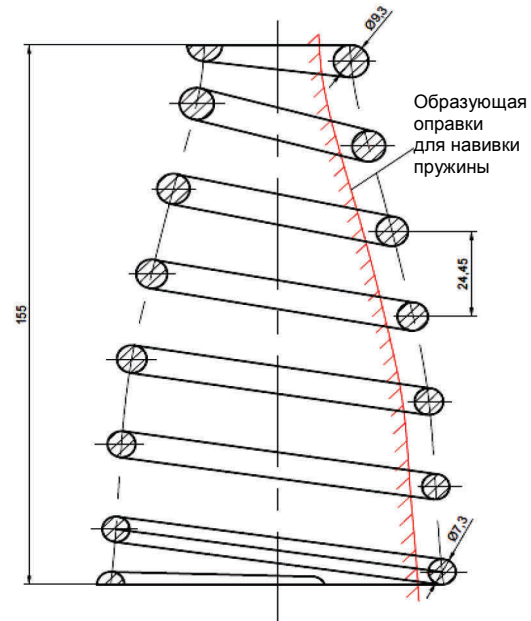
Конструкция пружины для силового замыкания сателлита (пассивный элемент) и центрального зубчатого колеса
